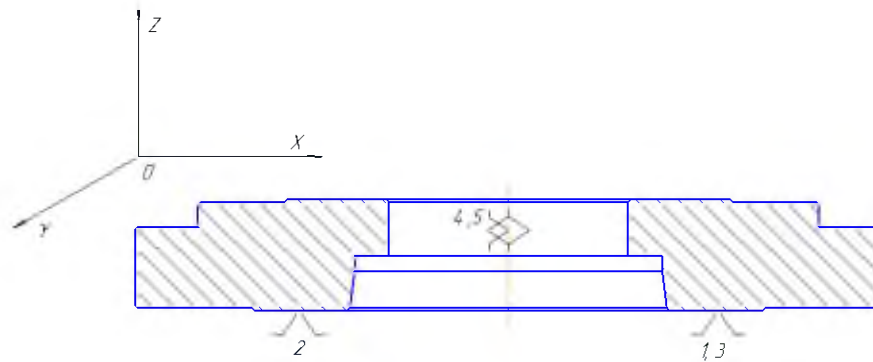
Базування для випадку оброблення поверхні правого торця і циліндричного отвору
